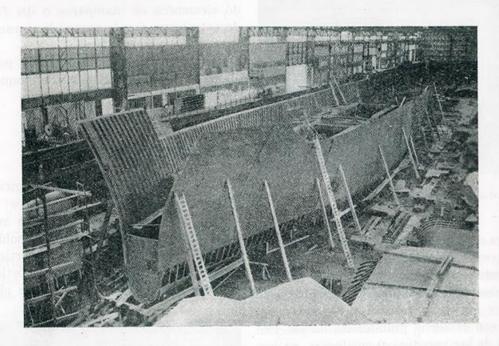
El "CAMBRAISEN" en armamento.—A babor un castillet.-andamio para las soldaduras de las juntas.
